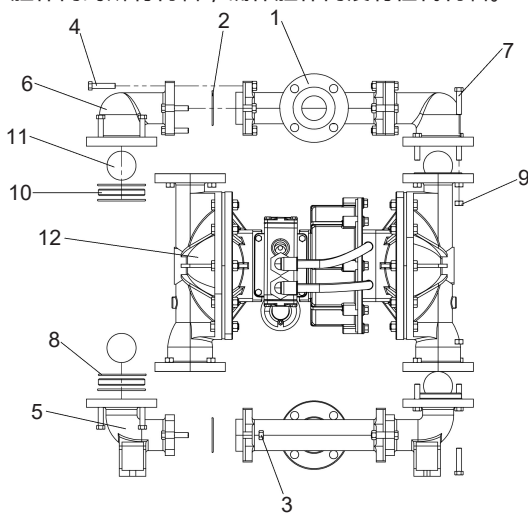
Disassembly of Inlet/Outlet进出口拆卸
